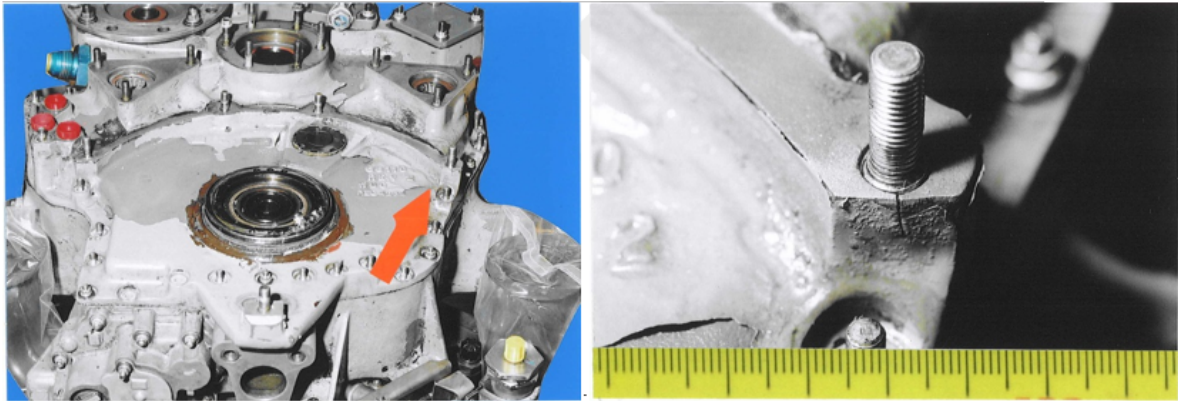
Getriebeseitiger Anschlussflansch des Abgasgehäuses: Verbindungsbohrungen in 4-Uhr- und in 8-Uhr-Position mit Abdrücken der Stehbolzen in den Bohrungen
